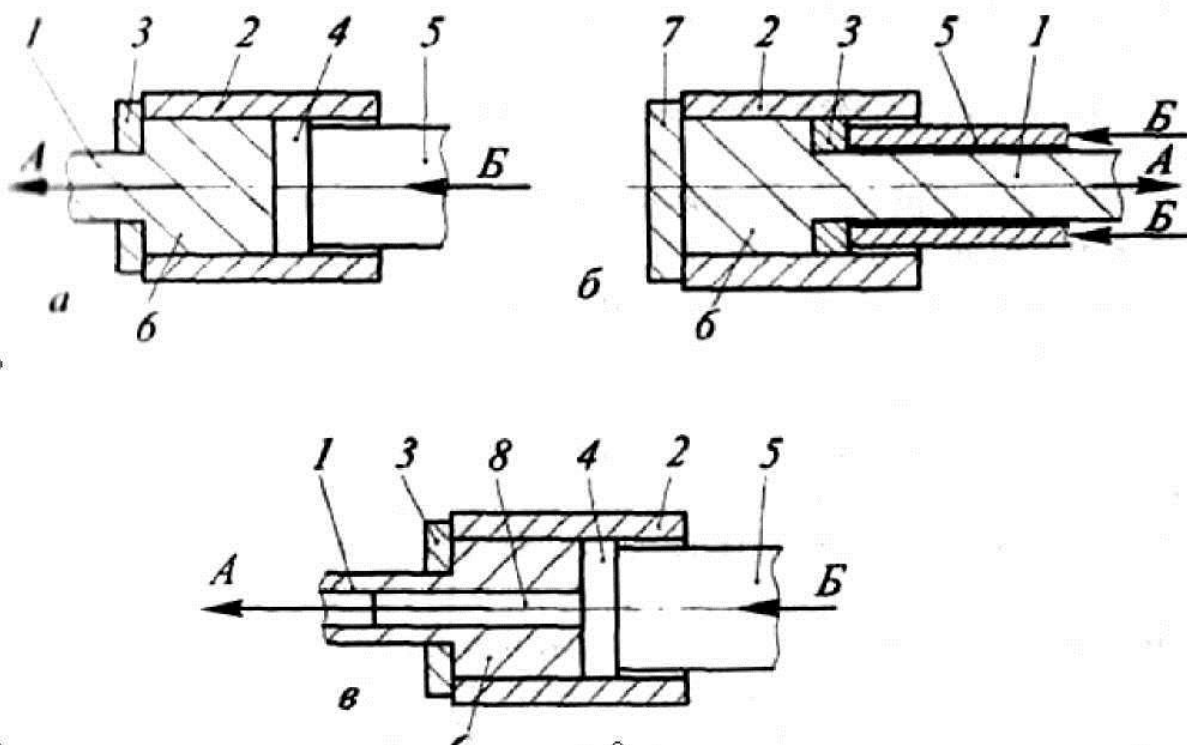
Прямий (а, в) і зворотний методи пресування: 1- виріб; 2 - контейнер; 3 - матриця; 4 - прес-шайба; 5 — пуансон; 6 — заготовка; 7 — кришка; 8 — голка
